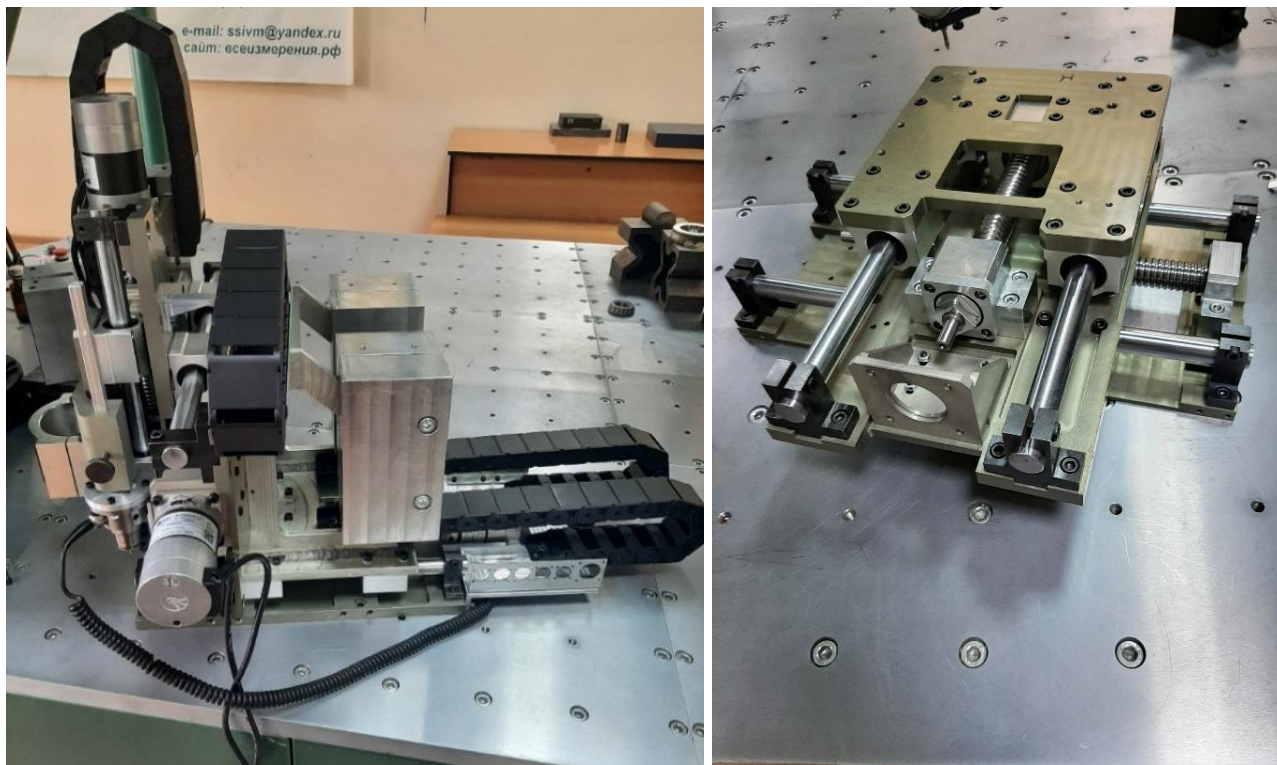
Внешний вид несущей системы опытного образца универсально фрезерного модуля в процессе сборки
